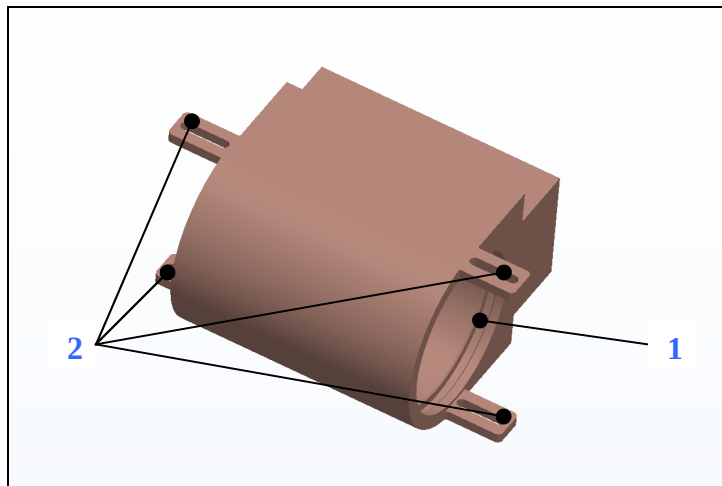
Tvar drážky v těle rozpěrného mechanismu
